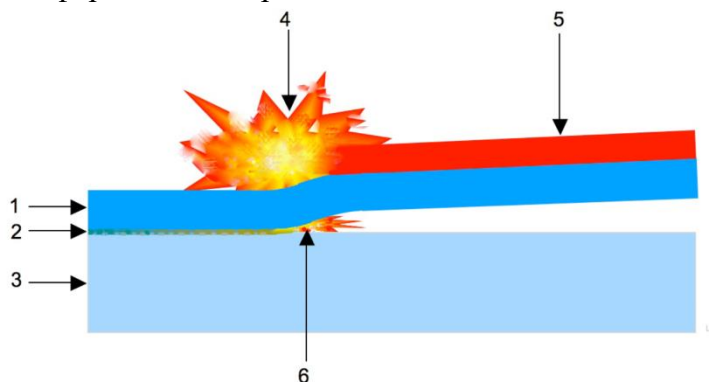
Схема сварки взрывом: 1 - подвижная деталь, 2 - сплавленная поверхность, 3 - неподвижная деталь, 4, 5 - взрывчатое вещество, 6 - кумулятивная струя
